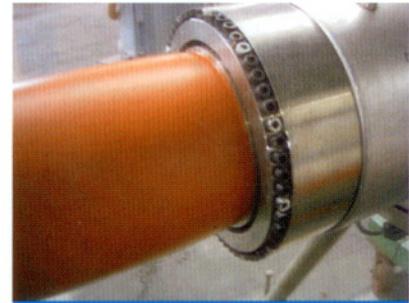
Rohrherstellung (110 mm Schaumkernrohr) mit einem ursprünglich thermisch zentrierten Rohrwerkzeug, das mit einer Flexringhülse nachgerüstet worden ist
